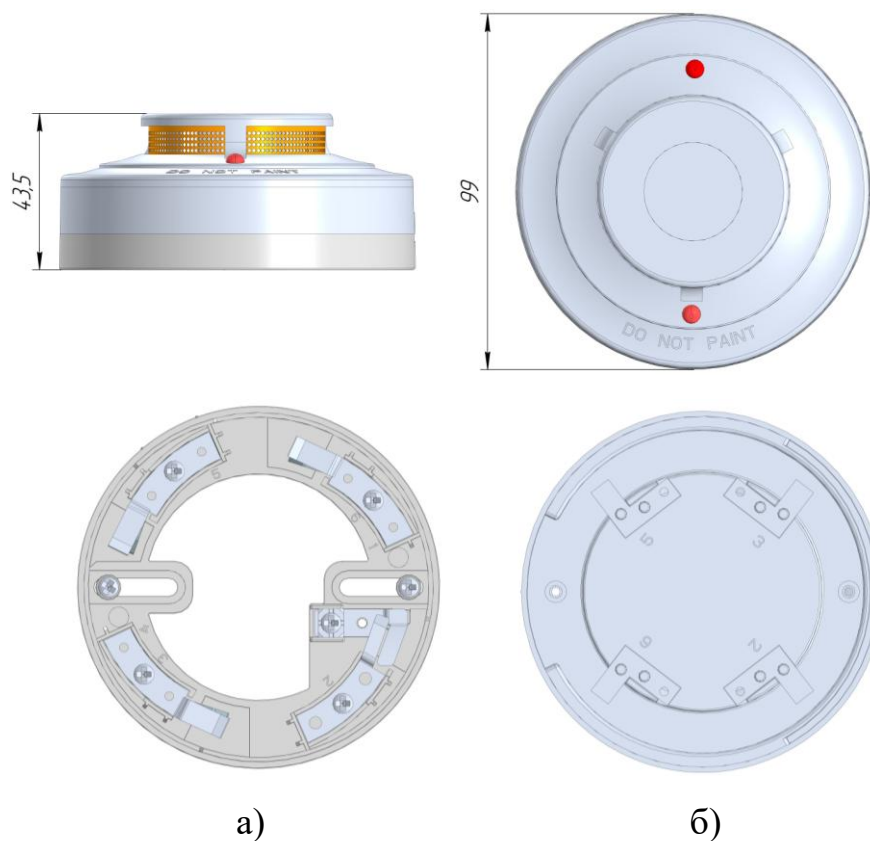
а - Общий вид извещателя пожарного дымового адресного «СПАРК» ИП212-01 а) стандартное базовое основание б) корпус
